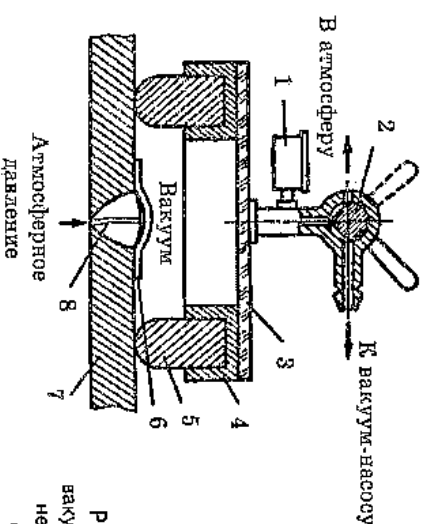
Схема вакуумного контроля непроницаемости сварного шва
